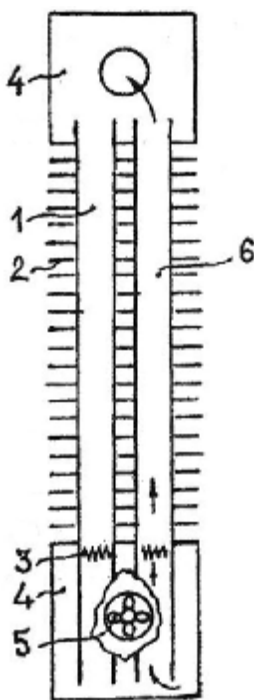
Разработана конструкция бытового нагревательного прибора, отличающегося особенностями расположения электронагревателя и вентилятора
